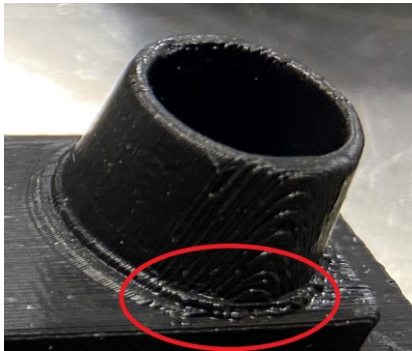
difetto nel sistema di fissaggio a clip durante lo stampaggio
